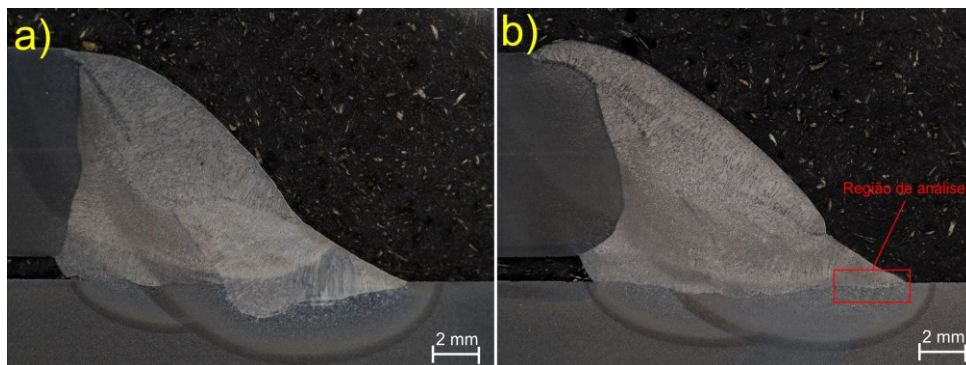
Macrografia de soldagem com pré-aquecimento por indução de 200 °C. Em a) GMAW-P DC; b) GMAW-P AC.
